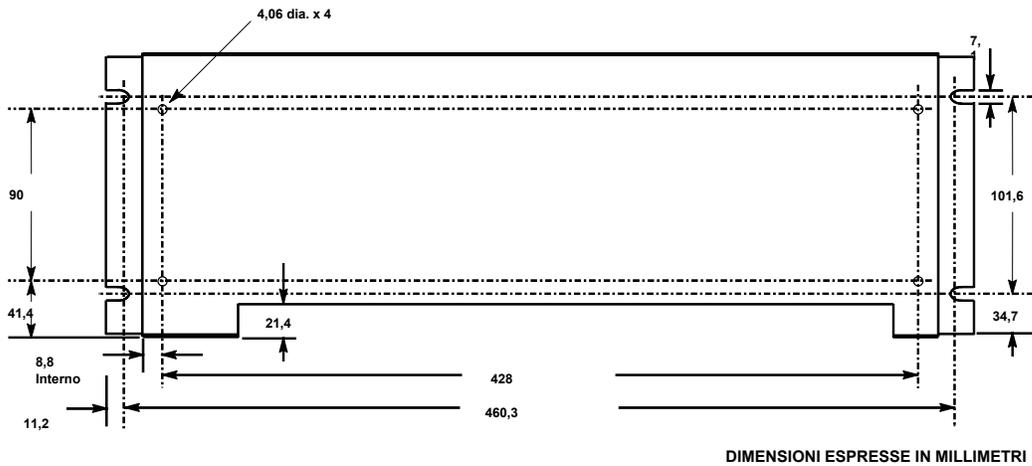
Sostegno adattatore per il montaggio a parte IC693ACC313
